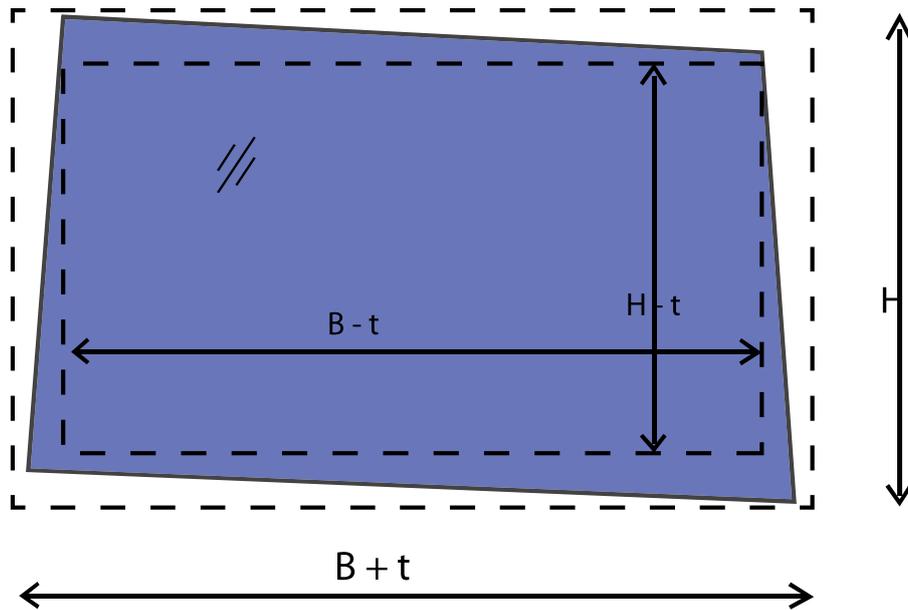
Rectangles de tolérance des dimensions livrées et des dimensions découpées finales. La tolérance des dimensions livrées et des dimensions découpées finales est différente. Elle dépend en outre de l'épaisseur nominale et de la longueur des côtés H ou B.
